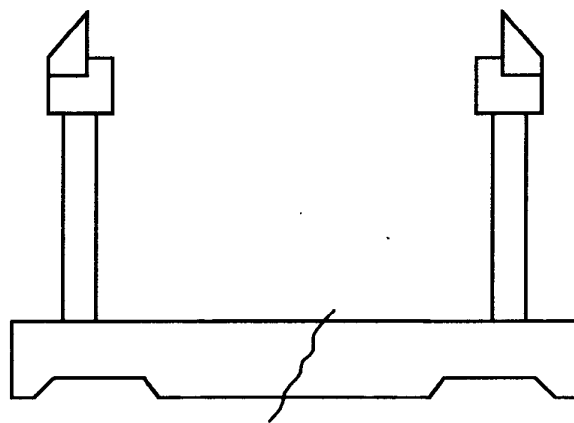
Приспособление для статической балансировки коленчатого вала с маховиком и сцеплением
